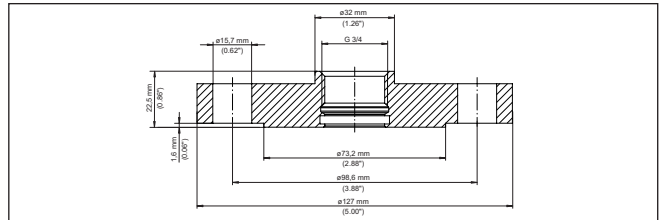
Maße Gewindeadapter G¾ (DIN 3852-X) auf Flansch 1½" (ASME B16.5, RF) 150 lb
